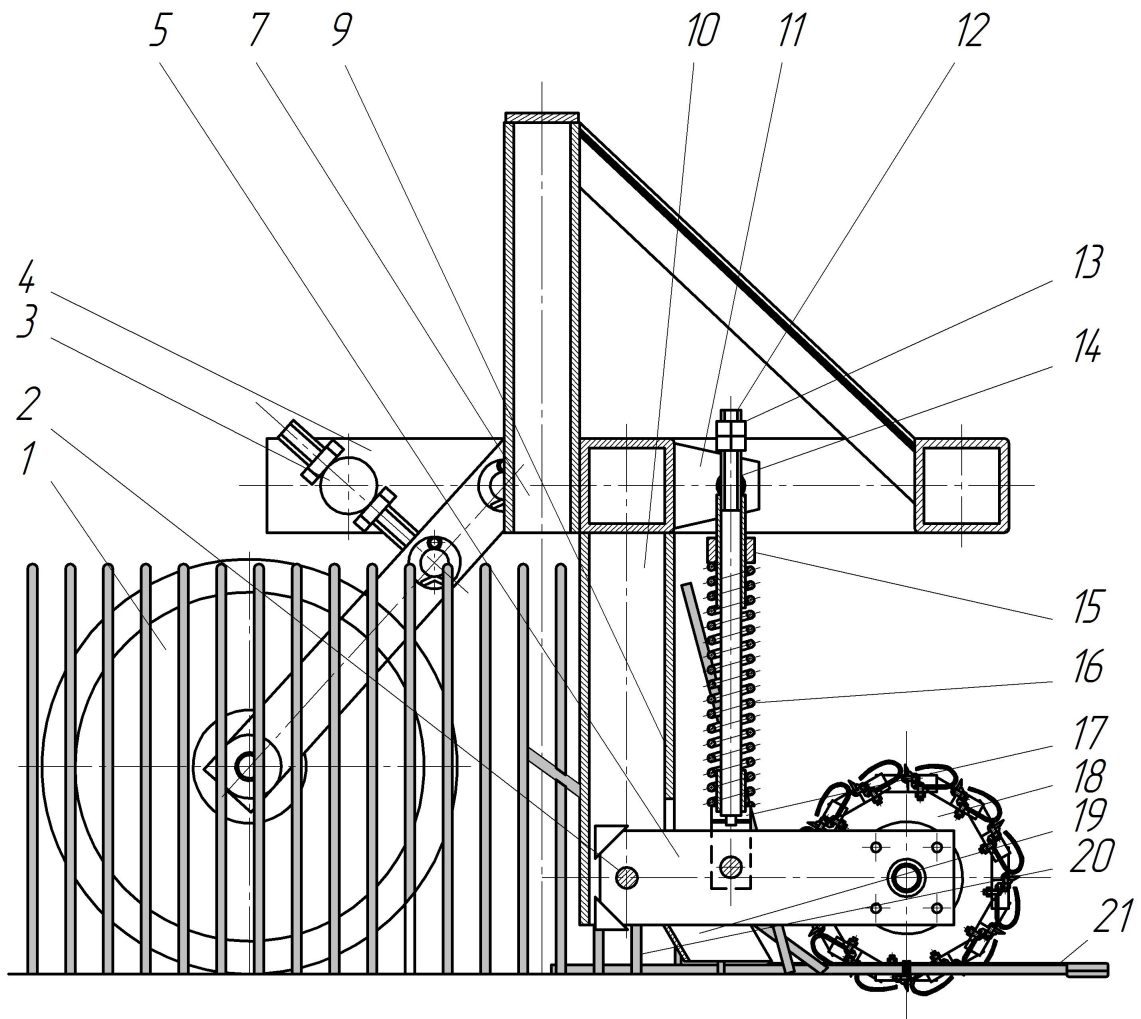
Різак-мульчувач рослин з барабанно-ножевими роторами (поздовжній розтин): 1 – опорне колесо; 2 – гвинтовий механізм регулювання висоти розташування рами; 3 – рама; 4 – палець важеля; 5 – начіпний пристрій; 6 – консоль; 7, 8 – важелі проміжної і бокової опори; 9 – палець гвинтової тяги; 10 – вертикальна стійка; 11 – щока провущини; 12 – гвинтова тяга; 13 – обмежувальна гайка; 14 – шарнір з кулісою; 15 – рухома чашка; 16 – пружина; 17 – нерухома чашка; 18 – подільник рослинної маси; 19, 20 – правий і лівий ротор; 21, 22 – стояча і порізнана рослинна маса
